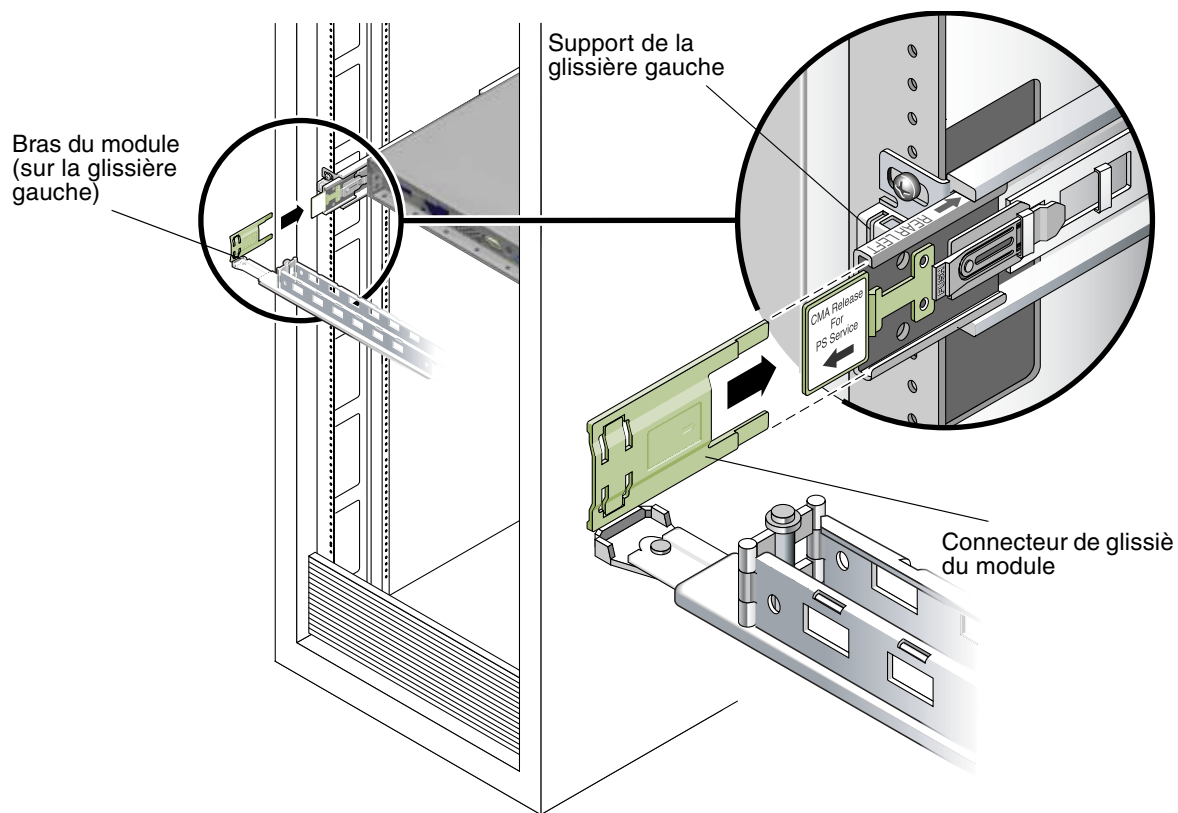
Insertion du connecteur de glissière à l'arrière du support de la glissière gauche
